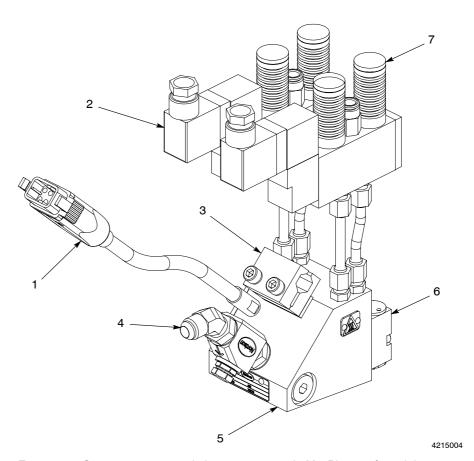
Componenti principali di una tipica pistola MiniBlue configurabile (nell'illustrazione una pistola a due moduli)
